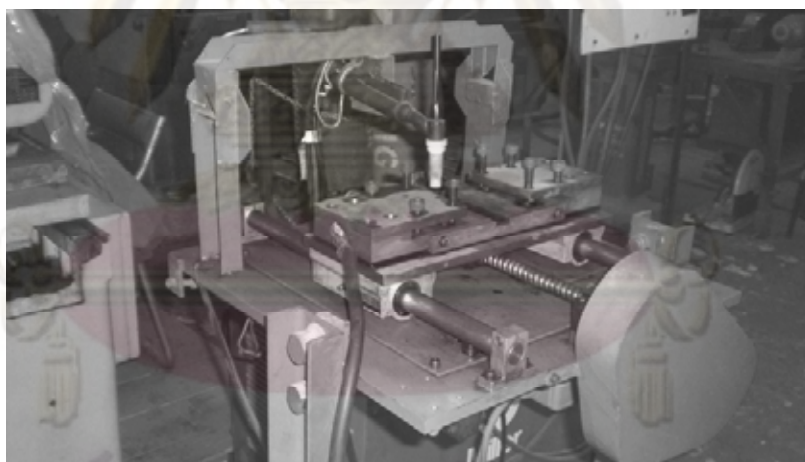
เครื่องเชื่อม Miller / Syncrowave 350 Ampere Constant Current AC / DC Arc Welding
